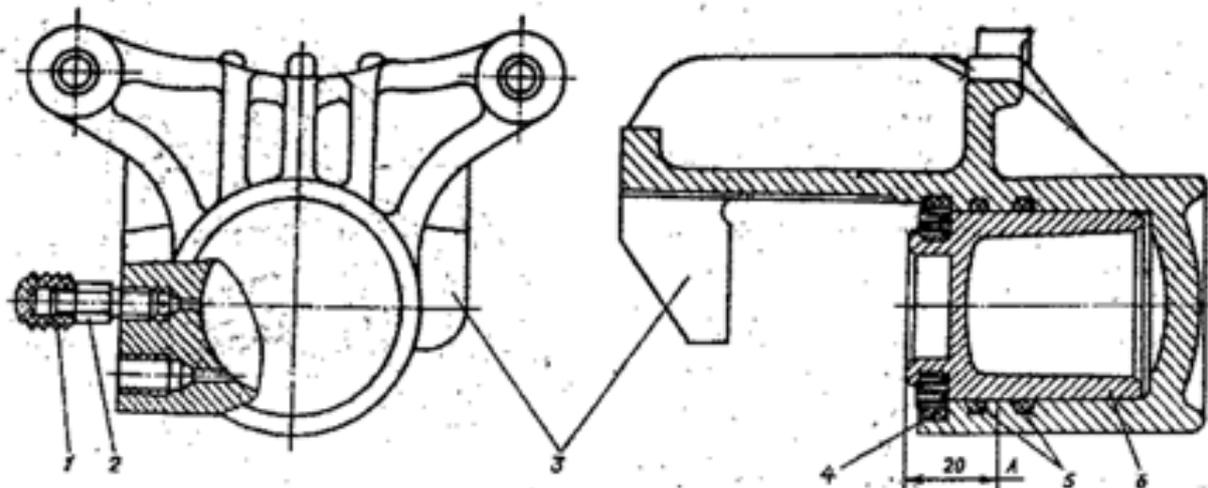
Скоба переднего тормоза в сборе: 1 - колпачок защитный; 2 - клапан выпуска воздуха; 3 - скоба; 4 - чехол защитный; 5 - кольцо уплотнительное поршня; 6 - поршень.
